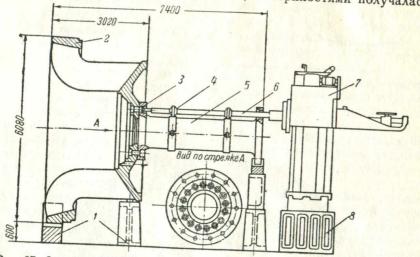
Приспособление для уравновешивания рабочего колеса.
